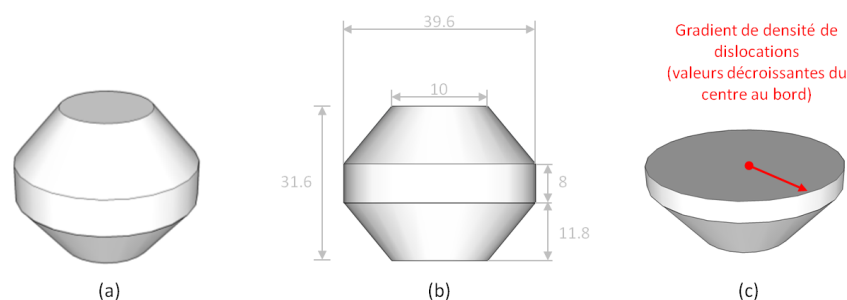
Vue 3D de l'éprouvette "double cône" (a) de ses dimensions (b) et de la localisation du gradient de densité de dislocations que l'on souhaite exploiter après déformation (c)
